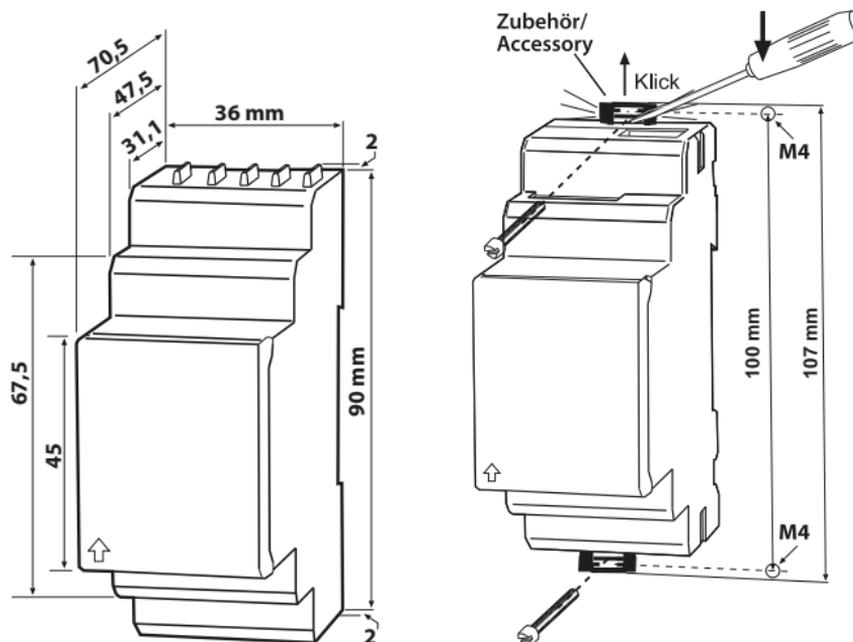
Maßbild, Skizze für Schraubbefestigung
